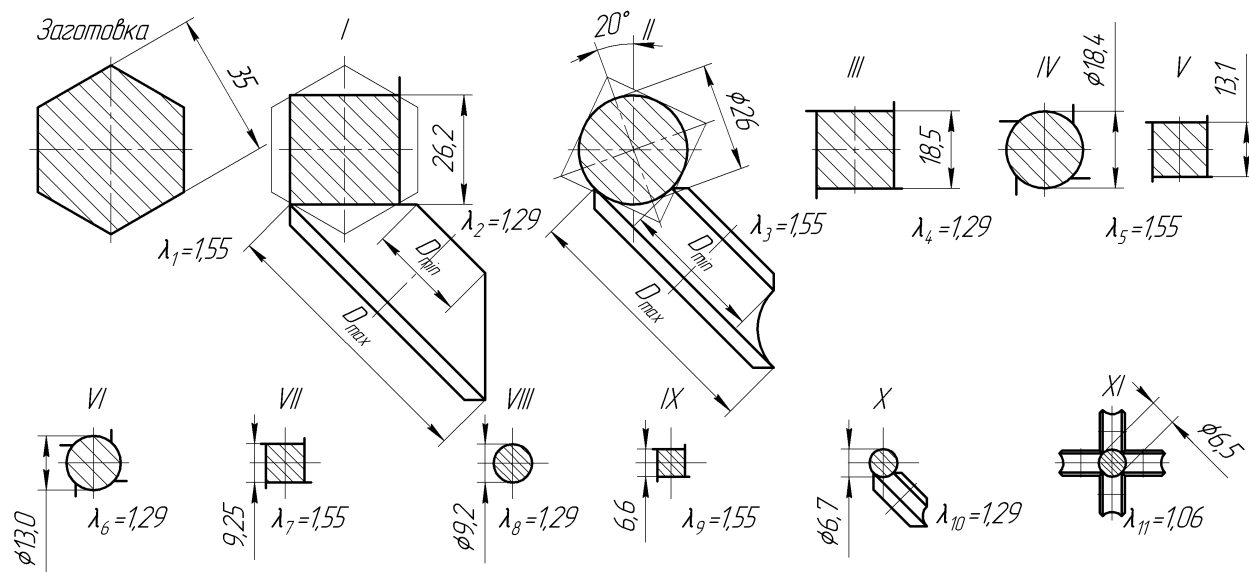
Схема калибровки для прокатки катанки в четырехвалковых калибрах конических валков
